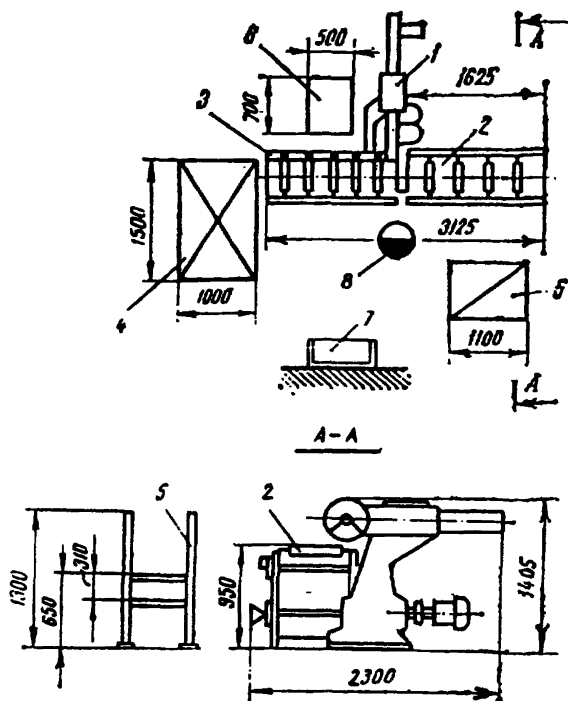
Схема планировки рабочего места станочника-распиловщика по облуживанию торцовочного станка ЦПА-40:
